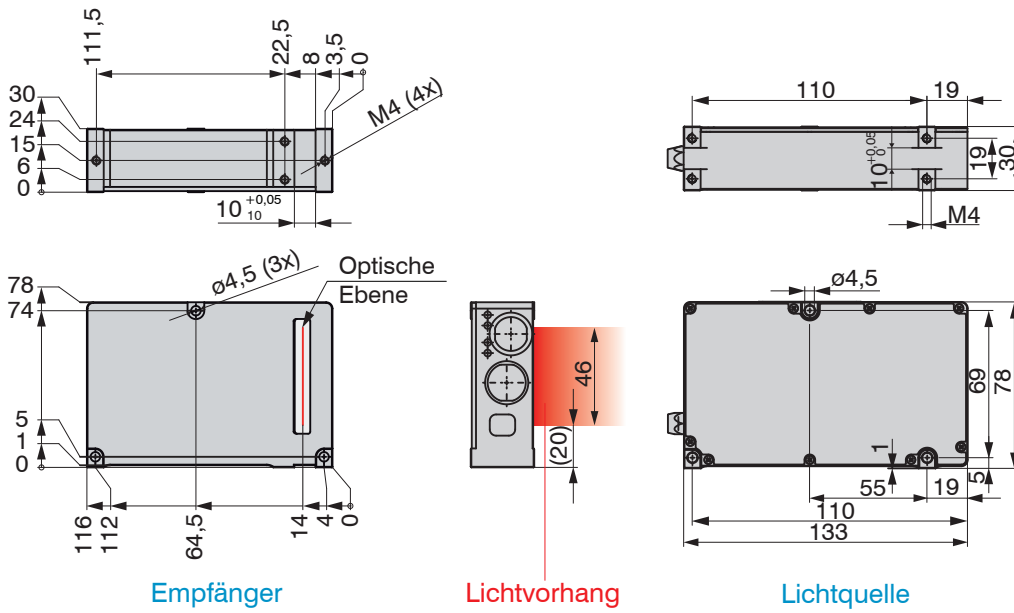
Maßzeichnung optoCONTROL 2520-46(090), Abmessungen in mm
